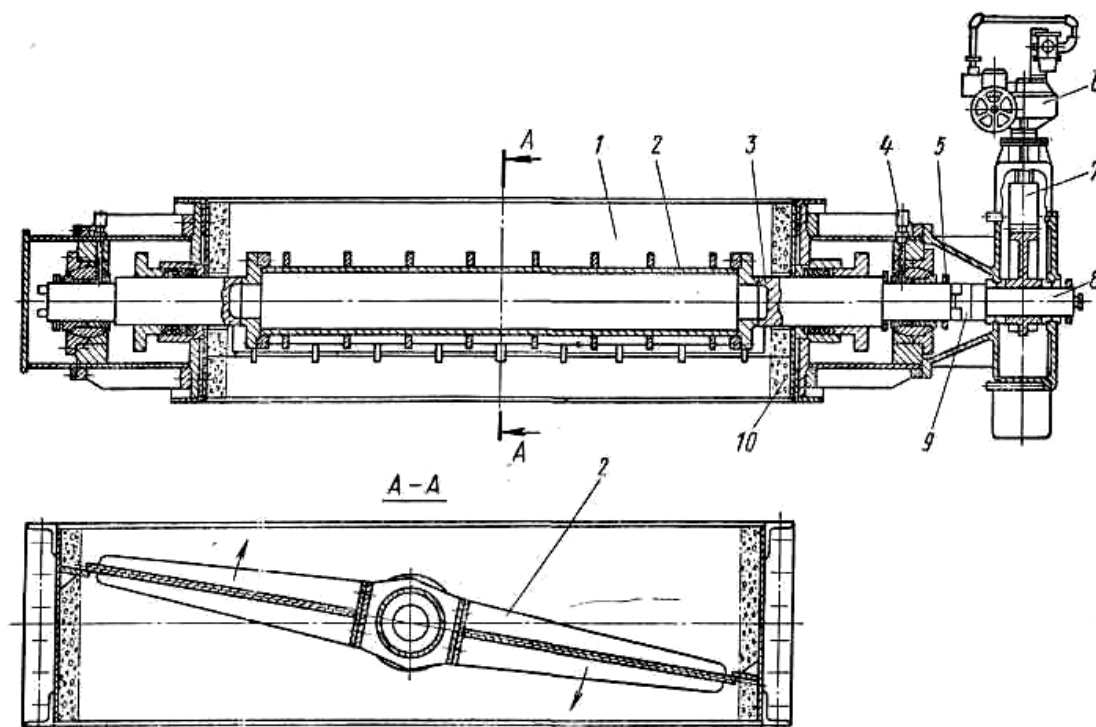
Заслонка поворотная для газоходов трубчатых печей
